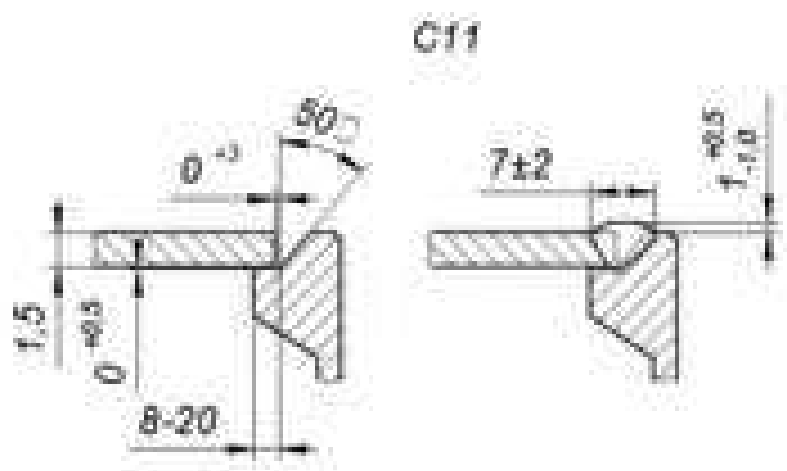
Эскиз стыкового сварного шва
